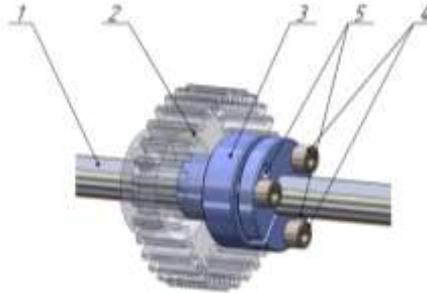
Схема закрепления зубчатого колеса с помощью конической закрепительной втулки KLLC015: 1 – вал; 2 – зубчатое колесо; 3 – коническая втулка KLLC015; 4 – винты для затяжки втулки; 5 – отверстия с резьбой для демонтажа втулки
